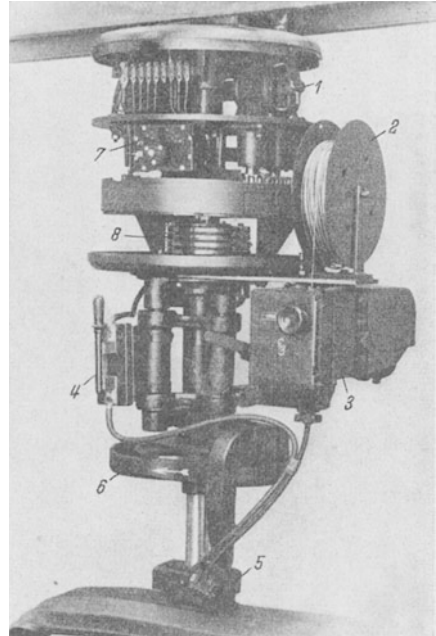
Schweißautomat für Schwellenschweißung.
